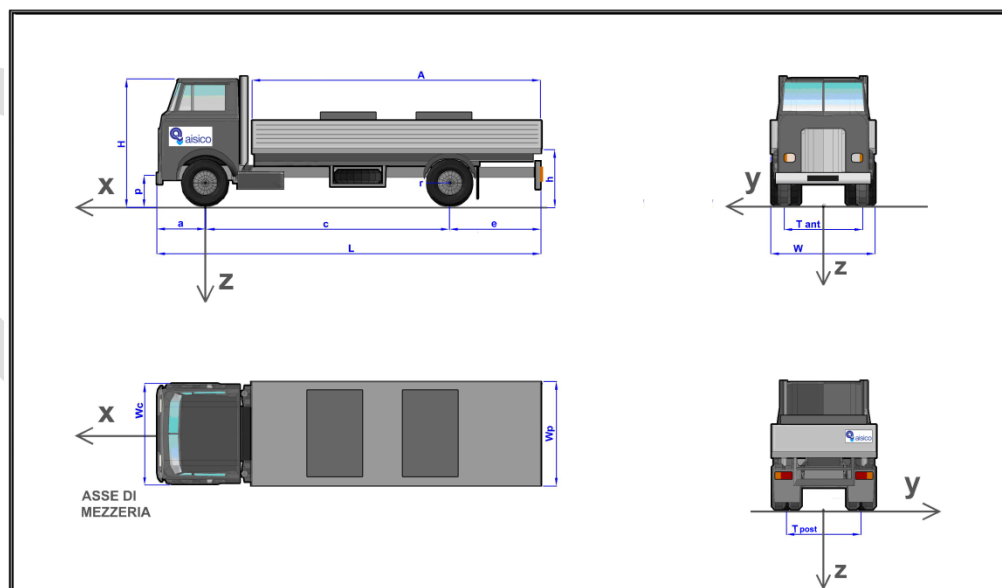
Figure 3 Dimensioni del veicolo – Vehicle dimensions
